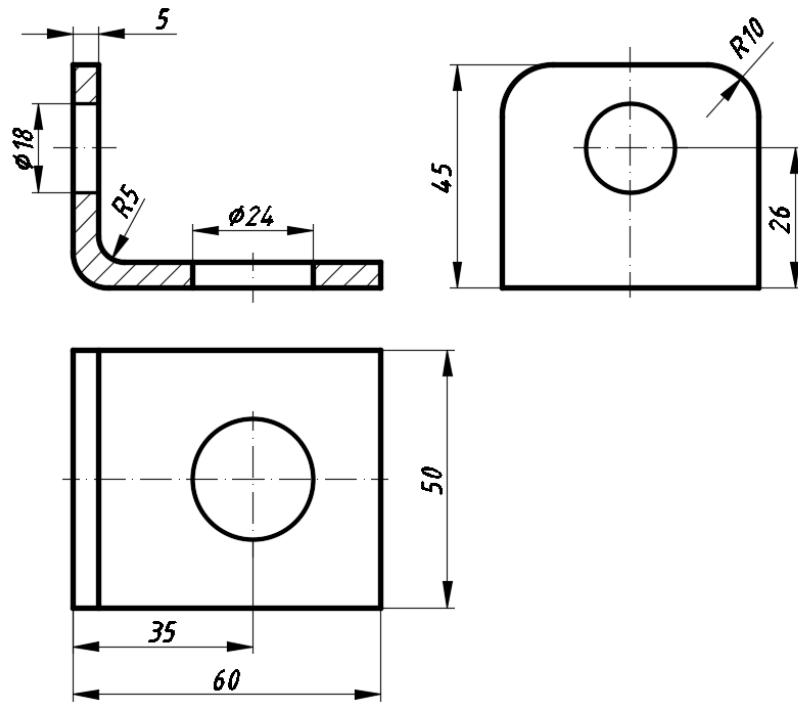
Образец выполнения чертежа детали, изготавливаемой гибкой.
